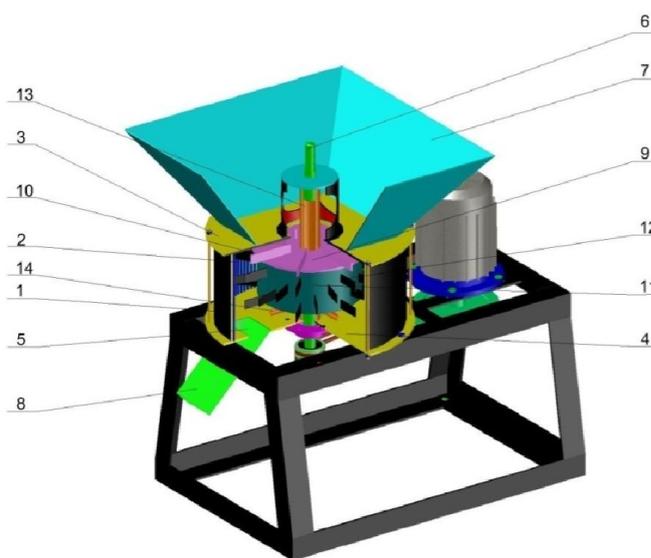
Компьютерная модель конструкции центробежной дробилки: 1-корпус; 2-отбойная поверхность; 3-крышка корпуса; 4-днище; 5-разгрузочное окно; 6-ротор; 7-загрузочная камера; 8-разгрузочный патрубок; 9-диск; 10-разгонные верхние лопатки; 11-цилиндрическая обечайка; 12-отбойные лопатки; 13-вал ротора.
